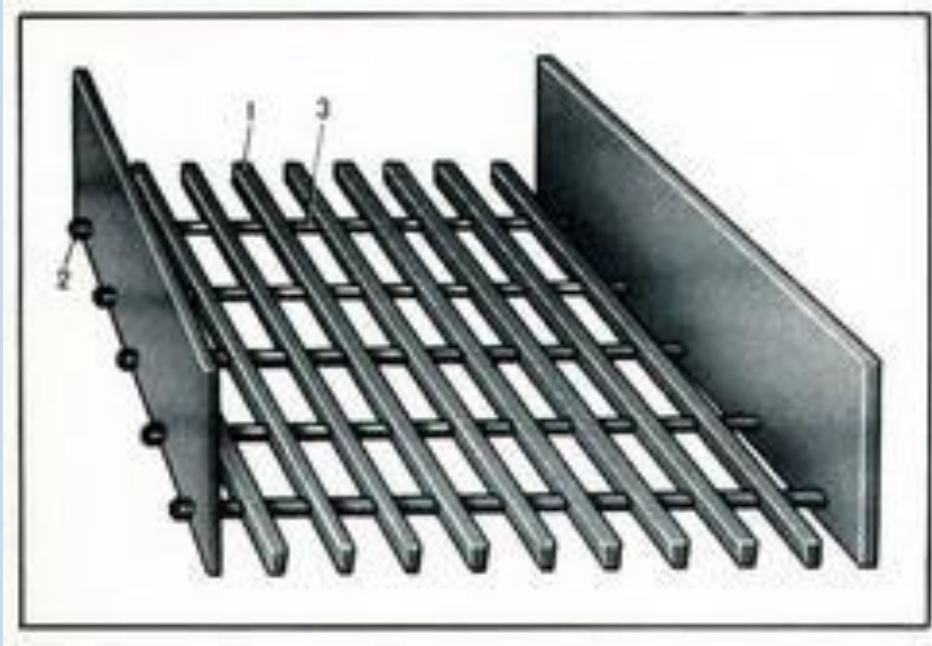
Составные части колосникового грохота: 1 - колосник; 2 - стяжной болт; 3 - распорная труба; [2]
